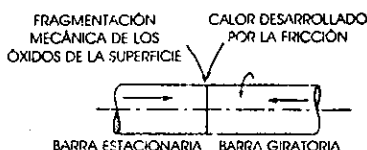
SOLDADURA POR FRICCIÓN
